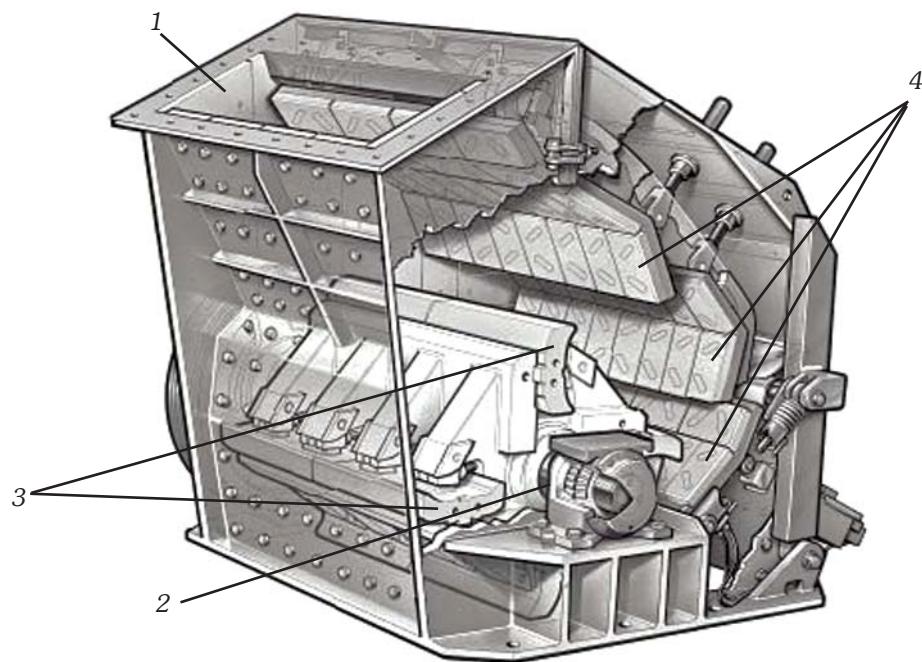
Дробилка роторная с горизонтальным расположением вала
